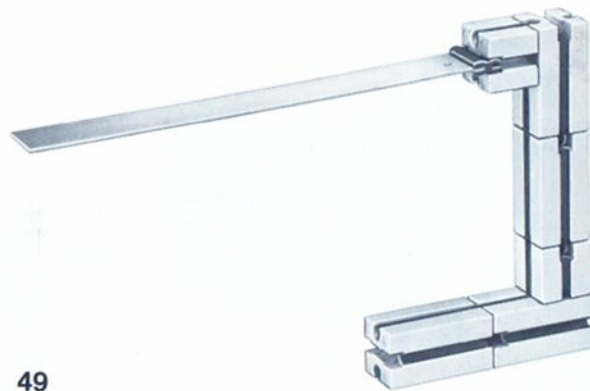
Beispiel für die Befestigung des Thermo-Bimetalls
